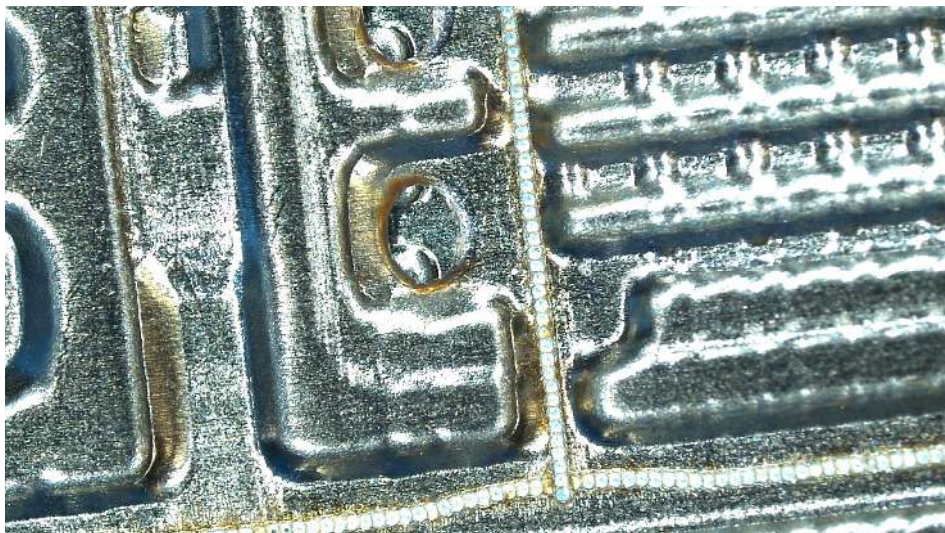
gepulstes Verfahren für Dichtnahtschweißung
